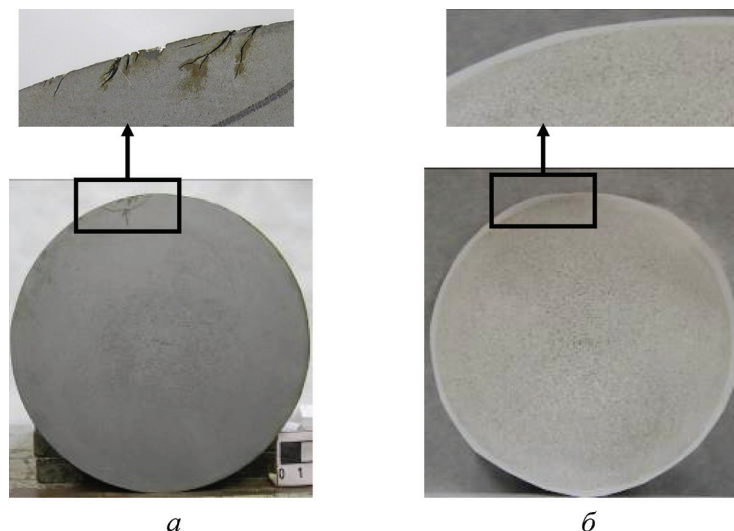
Поперечное сечение горячекатаной заготовки диаметром 140 мм из стали марки S355J2: а – серный отпечаток; б – макроструктура
